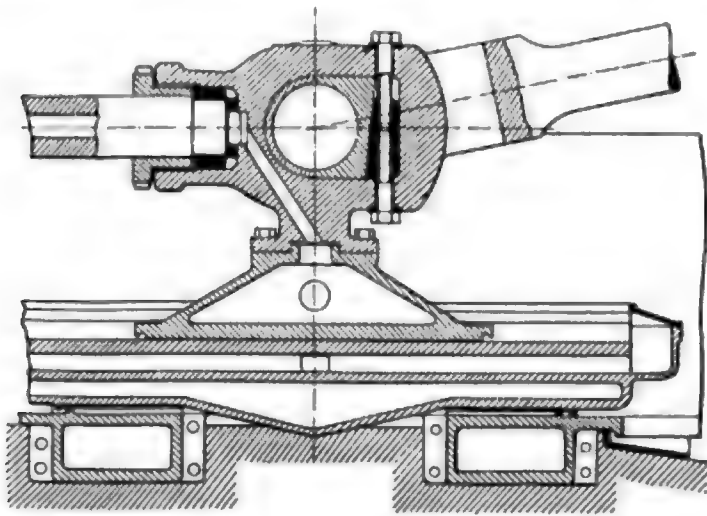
Befestigung der Kolbenstange im Kreuzkopf bei den Körttingmaschinen der Siegener Maschinenbau-Akt.-Ges. in Siegen.
